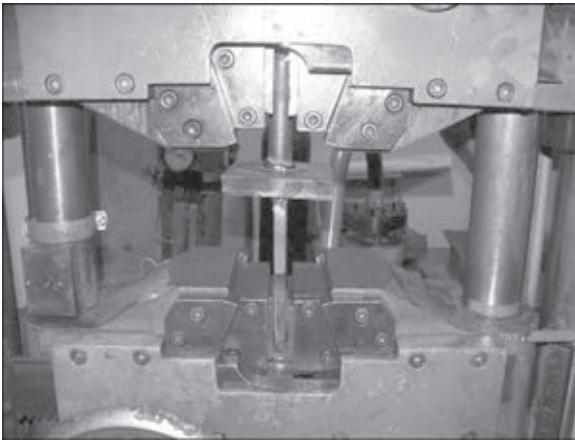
Испытание на усталость образца сварного соединения второй серии на машине ZDM-10pu
